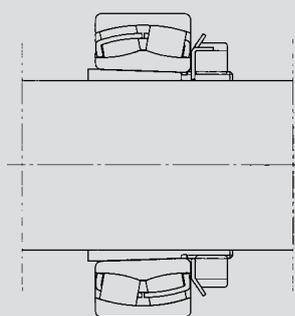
Цилиндрический вал, стопорная шайба (закрепительная втулка)
